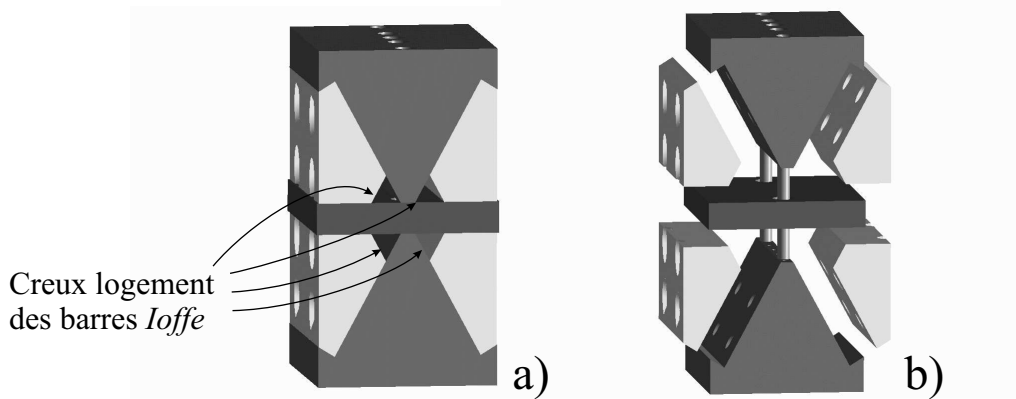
Schéma de la presse utilisée pour coller les barres Ioffe avec la forme correcte. a) vue assemblée de la presse, b) vue éclatée.
